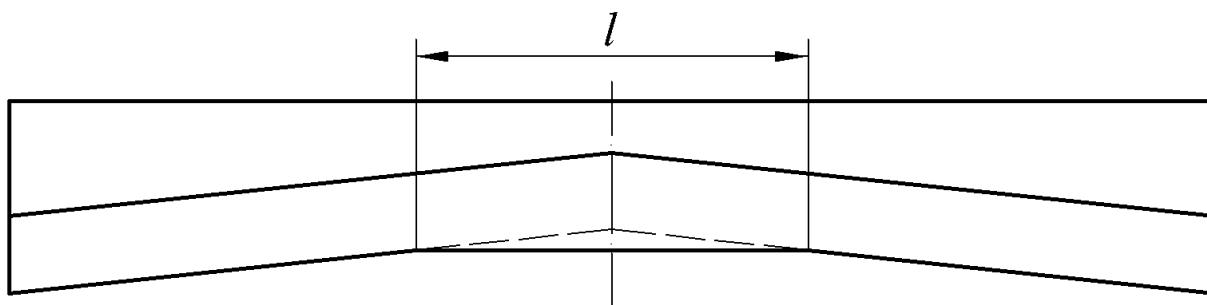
Шевронный нож со сложной формой режущей кромки конструкции «Северсталь» [81]
